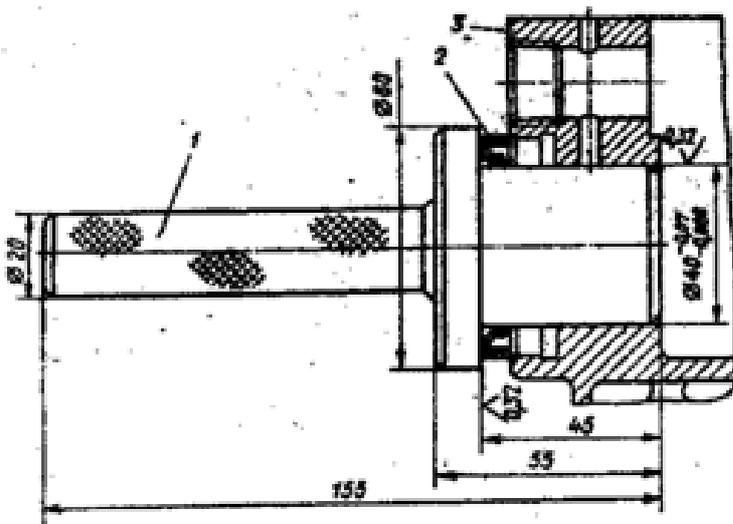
Запрессовка манжеты распределительного вала в головку цилиндров: 1 - оправка М9840-716; 2 - манжета; 3 - головка цилиндров
